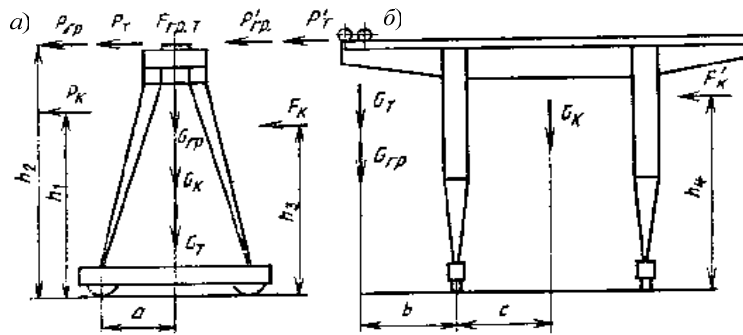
Расчетные схемы для определения грузовой устойчивости козловых двухконсольных кранов
